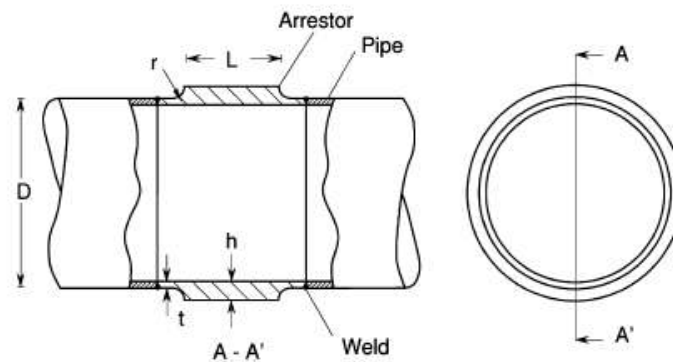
Esquema de um buckle arrestor soldado entre dois segmentos do tubo (LEE [6]).
